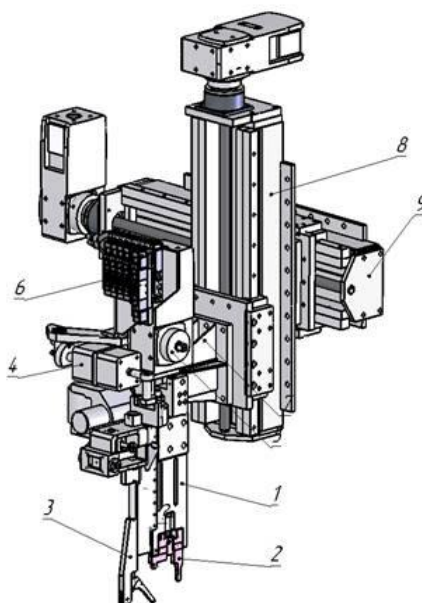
Состав сварочной головки АСУР
